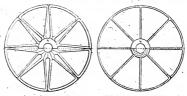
Roue en fer. Fig. 390. — Autre roue en
